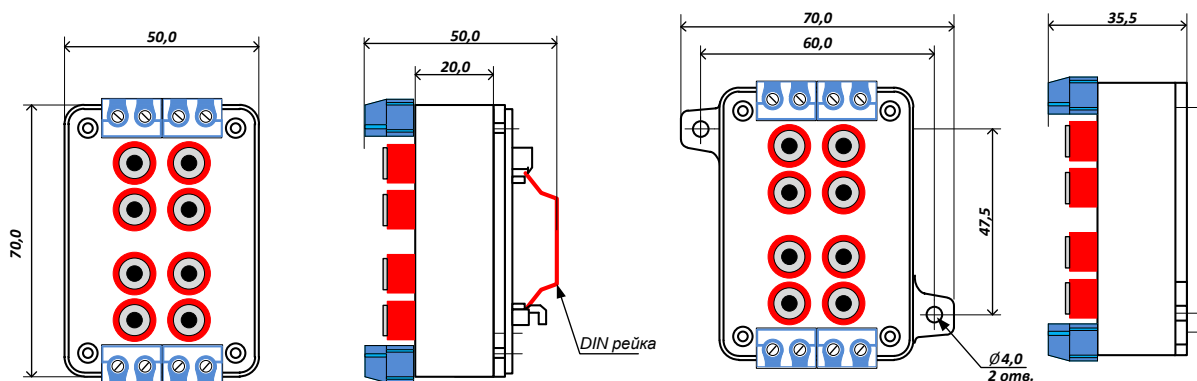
Габаритные и установочные размеры ВИМ 2x2;
